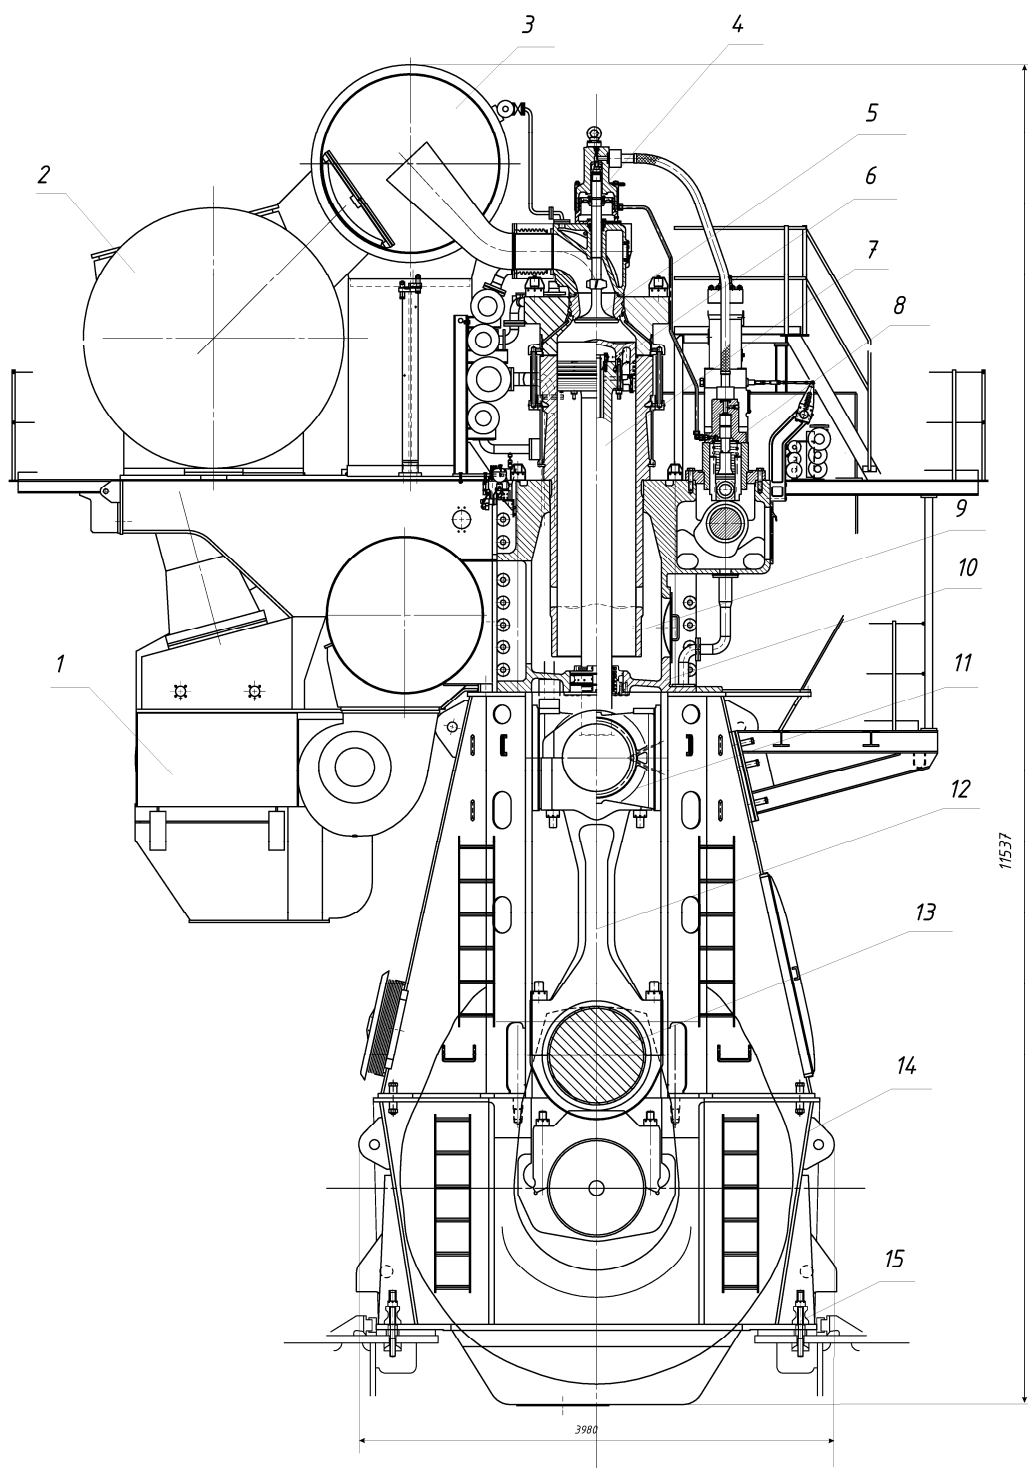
Двигуни 7ДКРН 70/236 фірми МАН (7L70MC-C) [2]: 1 – повітроохолоджувач; 2 – турбокомпресор; 3 – випускний ресивер; 4 – привід випускного клапану; 5 – випускний клапан; 6 – поршень; 7 – шток поршню; 8 – модулятор гідроприводу клапана; 9 – втулка циліндру; 10 – сорочка циліндру; 11 – крейцкопф; 12 – шатун; 13 – колінчатий вал; 14 – фундаментна рама; 15 – фундамент судна
